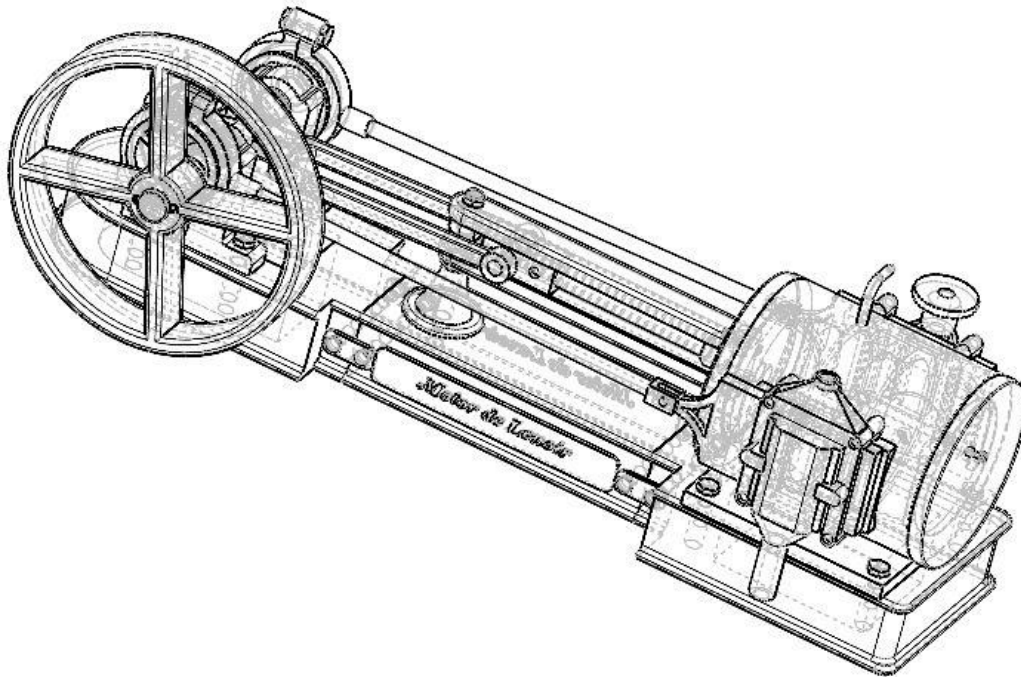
Ensamblaje del motor visto desde la entrada de combustible.
